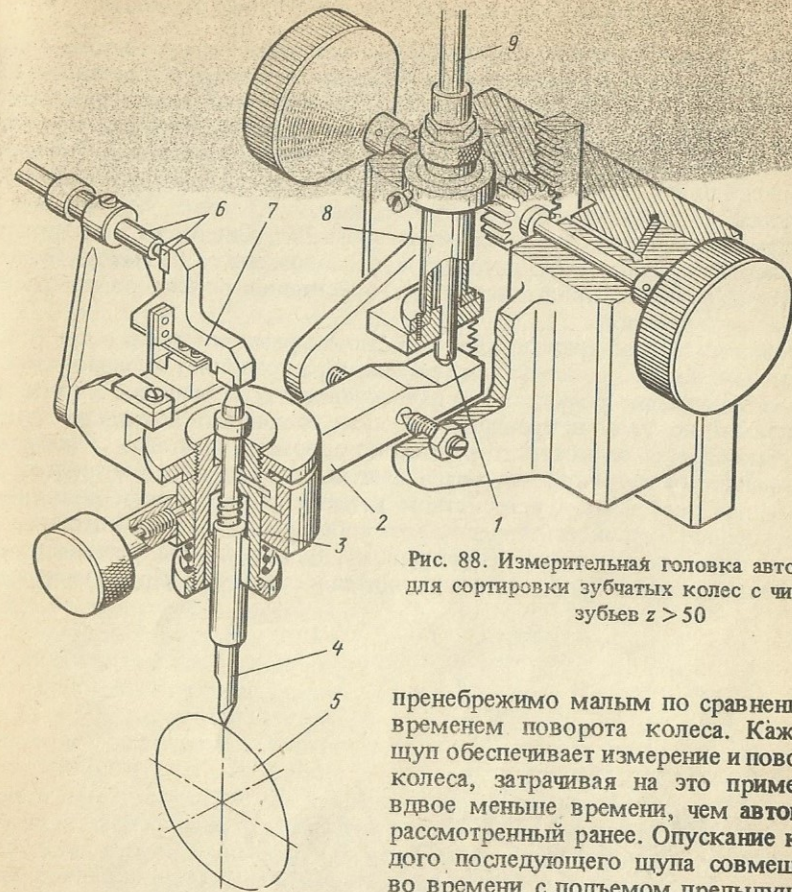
Измерительная головка автомата для сортировки зубчатых колес с числом зубьев $z > 50$
